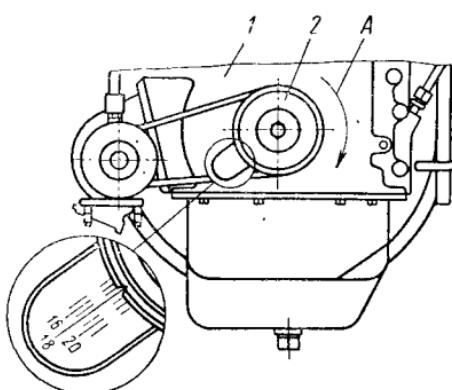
Совмещение рисок на шкиве коленчатого вала и крышке шестерен распределения:
